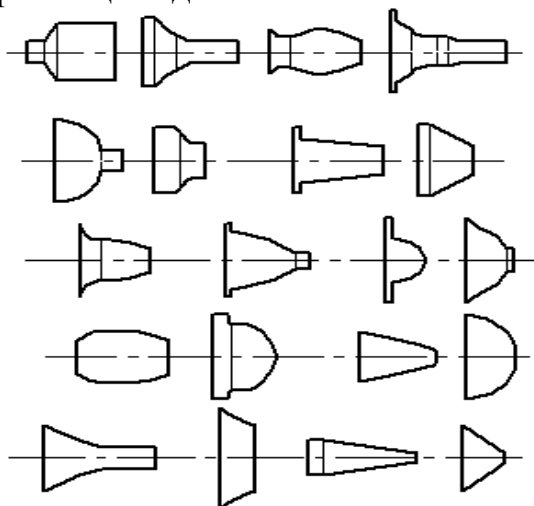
Деталі, що виготовляються ротаційної витяжкою
